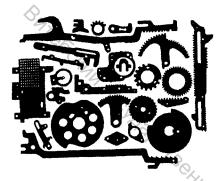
Типы заготовок, изготовляемых чистовой вырубкой
